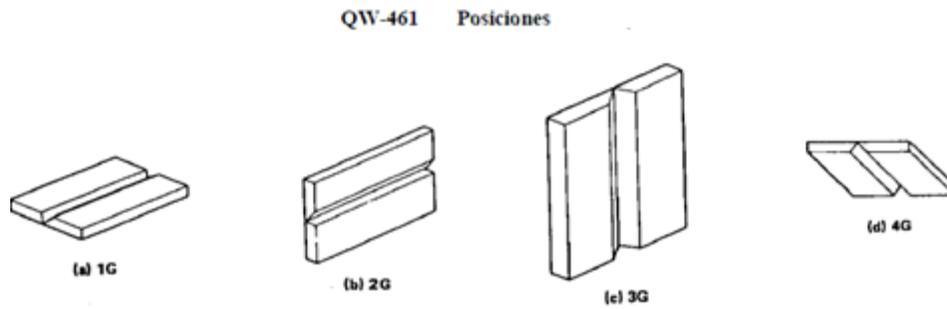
QW-461.3 POSICIONES EN SOLDADURA DE RANURA. (A) POSICIÓN 1G.
